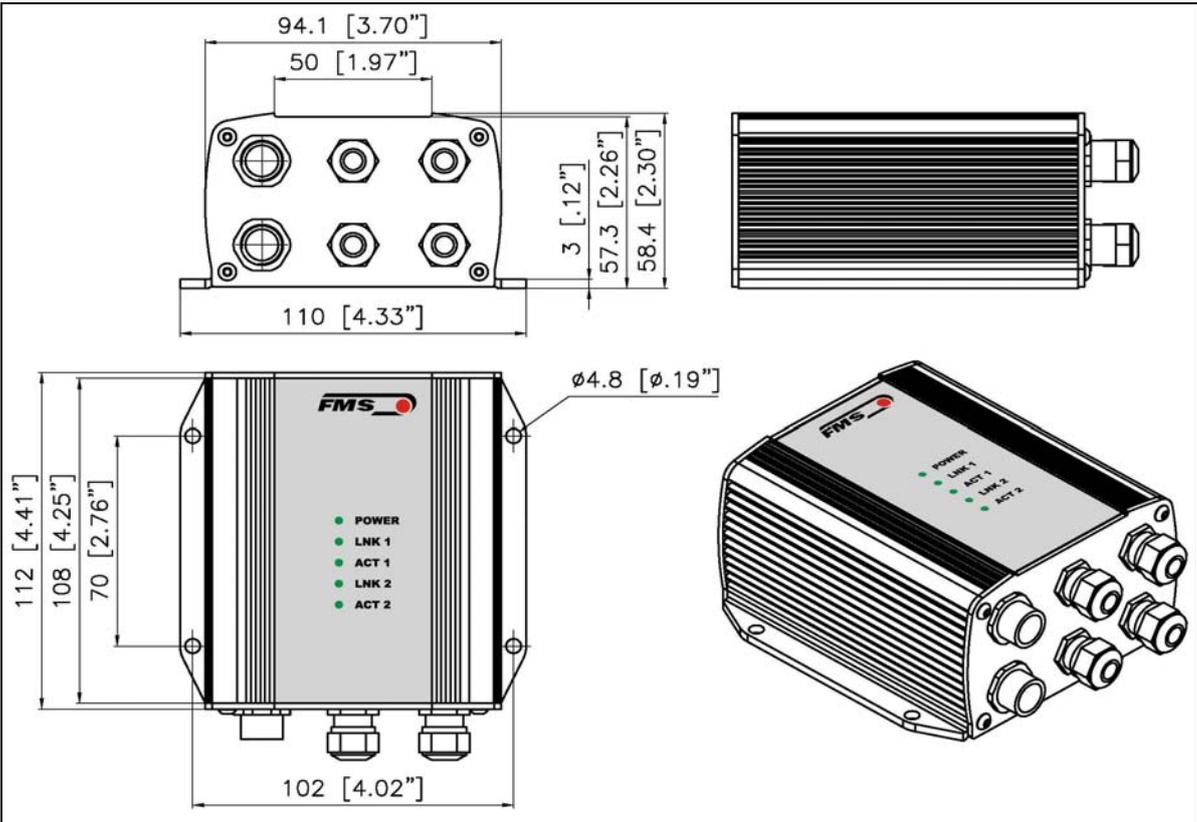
EMGZ 490.W Gehäuse für Wandmontage
